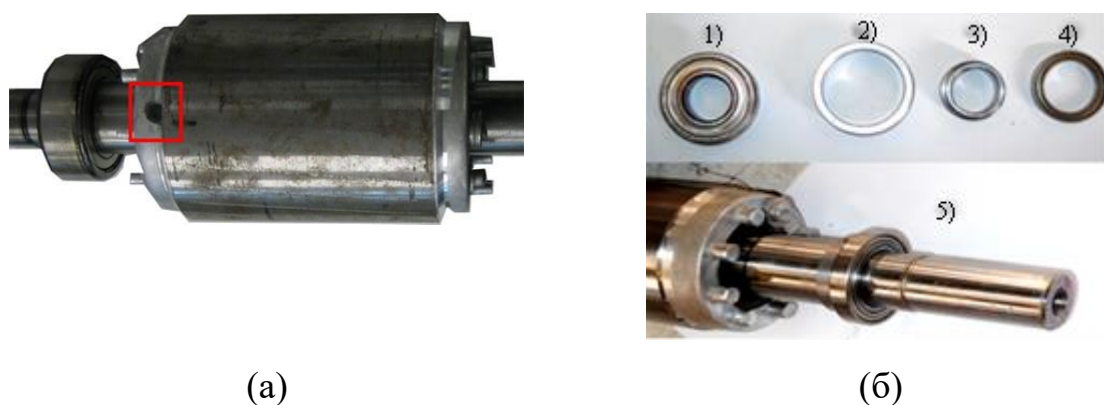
Экспериментальные АД: а) – ротор с дефектом в одном стержне; б) – ротор с эксцентриситетом: 1) – оригинальный подшипник; 2) – наружная эксцентриковая втулка; 3) – внутренняя эксцентриковая втулка; 4) – новый подшипник; 5) – втулки и подшипник, установленные на валу
